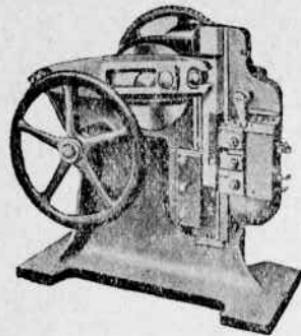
Резьбонакатный полуавтомат с магазином.
